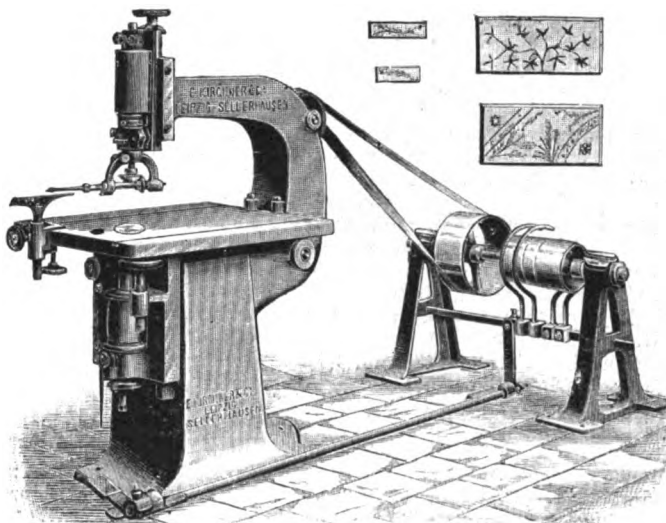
Universal-Fräsmaschine mit Apparat für Schnitz- und Bildhauerarbeiten.
